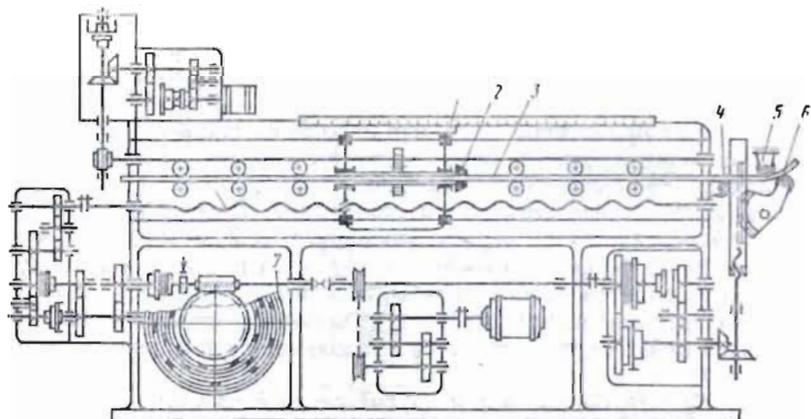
Кинематическая схема трубогибочного станка с программным управлением ТГПС-3
